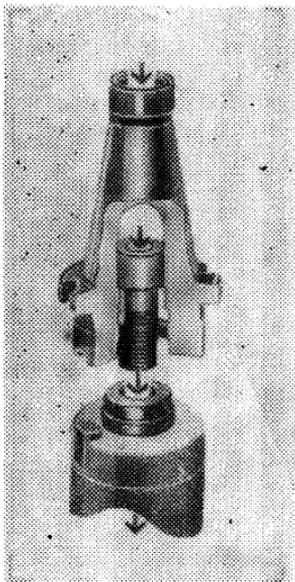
Пример типового конструктивного решения агрегатирования инструмента с внутренним подводом СОЖ
